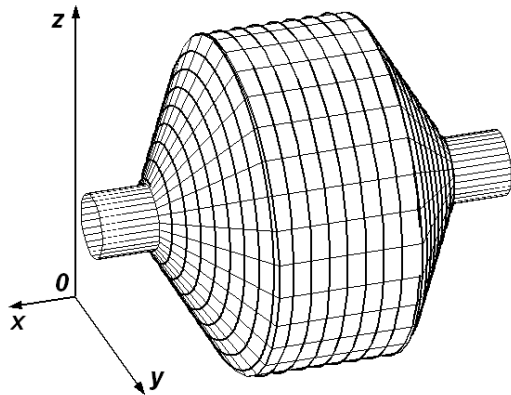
Біциліндроконічний барабан з лініями навивки каната на його робочих поверхнях.
